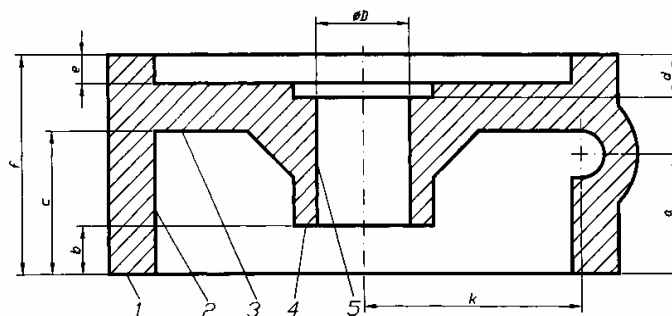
Система простановки размеров и последовательность обработки поверхностей заготовки
